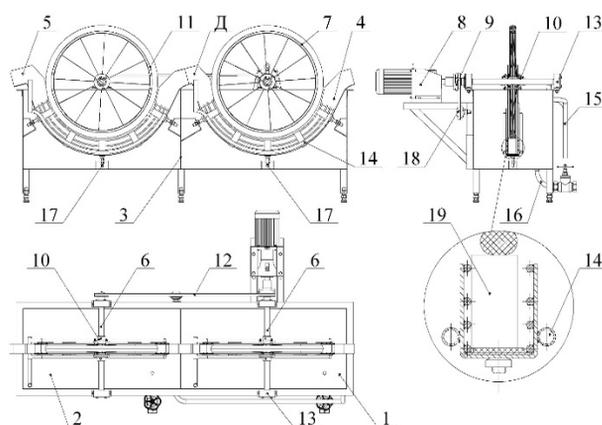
Конструкция предлагаемой машины для мойки банок:
